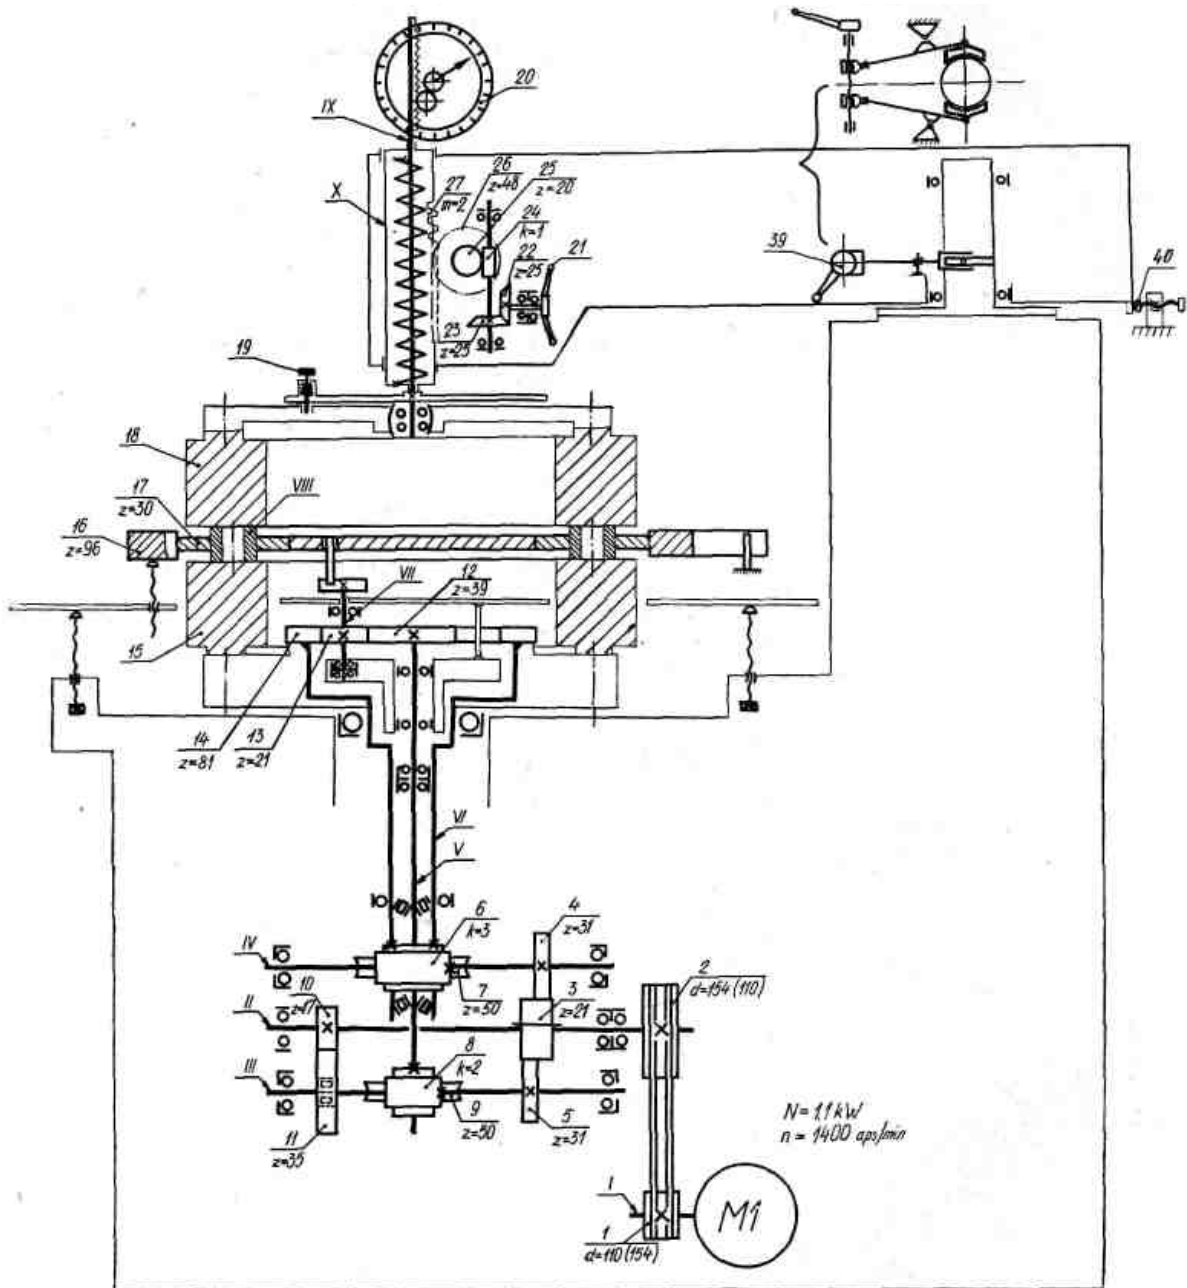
Кинематическая схема универсального притирочного станка модели 3Б814
